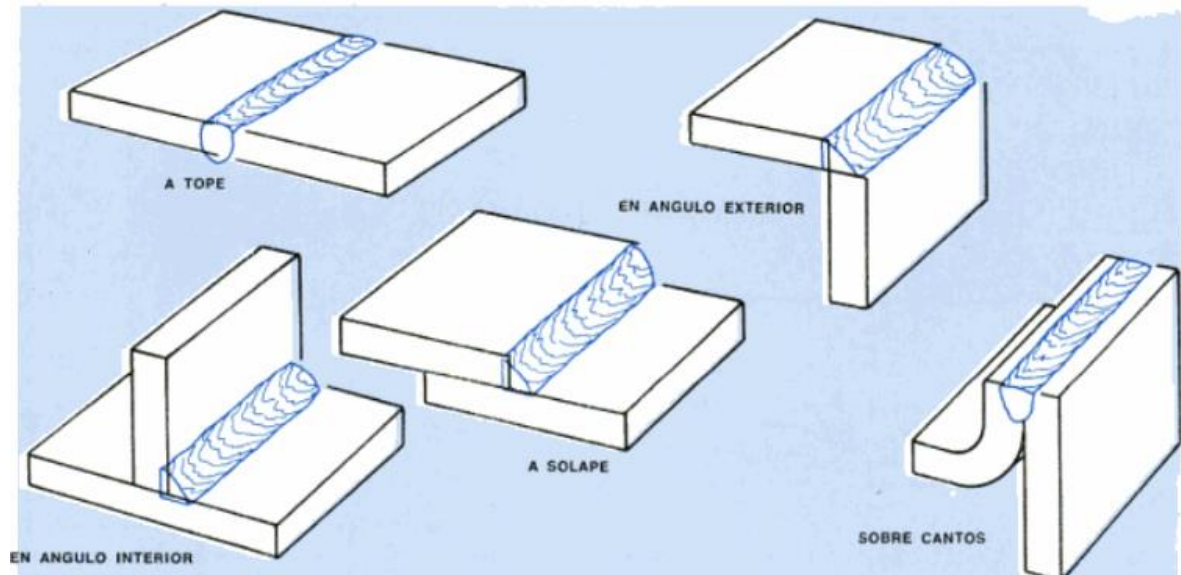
Tipos básicos de uniones de soldadura (Técnica y práctica de la soldadura Cap.4).
